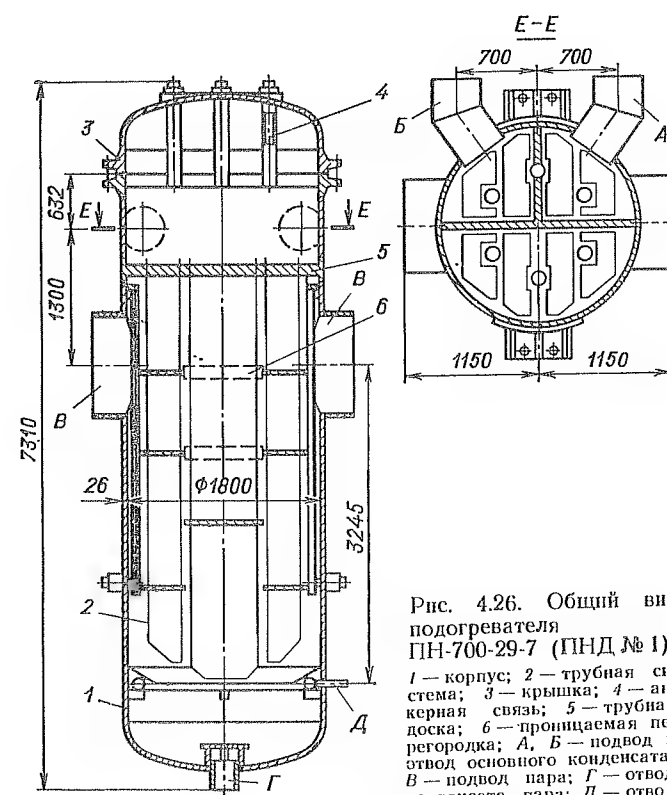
Общий вид подогревателя ПН-700-29-7 (ПНД № 1): 1 — корпус; 2 — трубная система; 3 — крышка; 4 — анкерная связь; 5 — трубная доска; 6 — проникаемая перегородка; А, Б — подвод и отвод основного конденсата; В — подвод пара; Г — отвод конденсата пара; Д — отвод паровоздушной смеси
